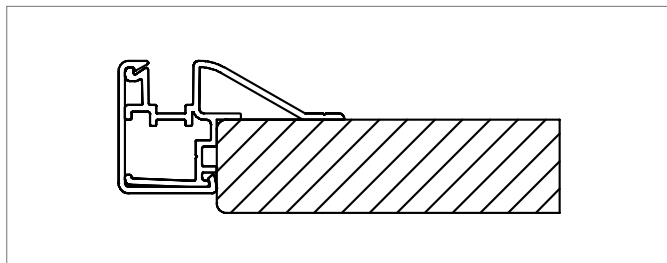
Querschnitt Führungsschiene auf Platte
